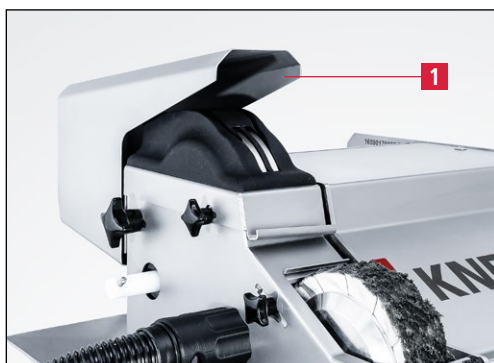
Приспособление для заточки ручных ножей HV 150
